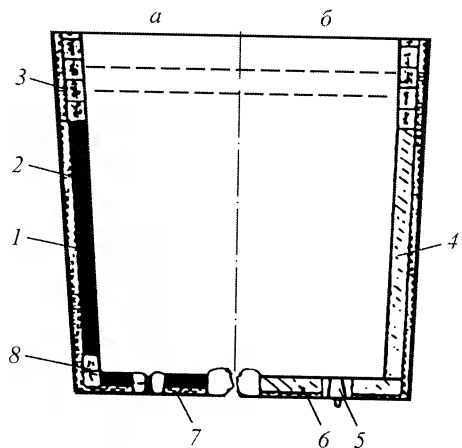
Общая схема футеровки сталеразливочного ковша агрегата ковш-печь:
